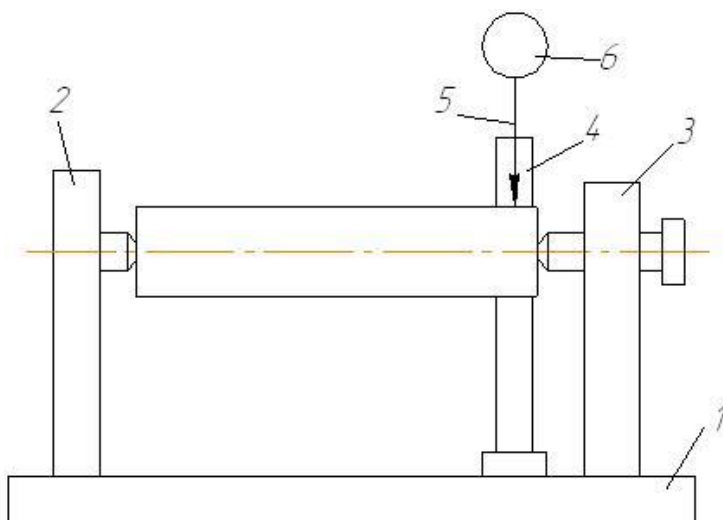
Схема контрольного приладу: 1-плита; 2-бабка нерухома; 3-бабка рухома; 4-стійка; 5-державка; 6-індикатор
